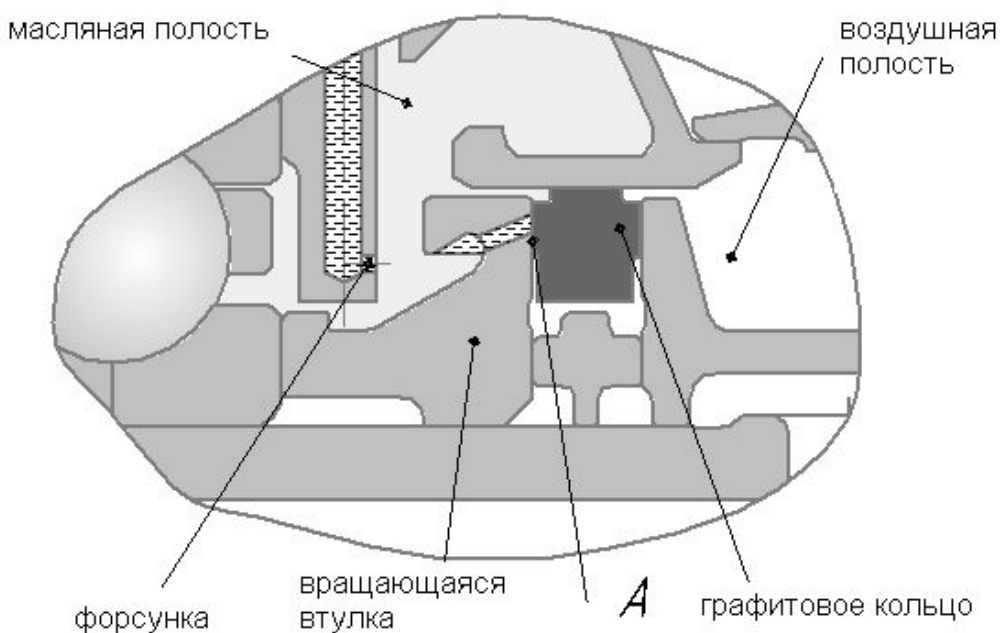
Конструкция уплотнения опоры ротора компрессора
